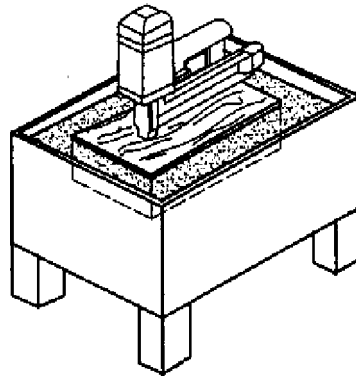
Інструмент для встановлення кріпильних деталей. Устаткування випробувального стенда
